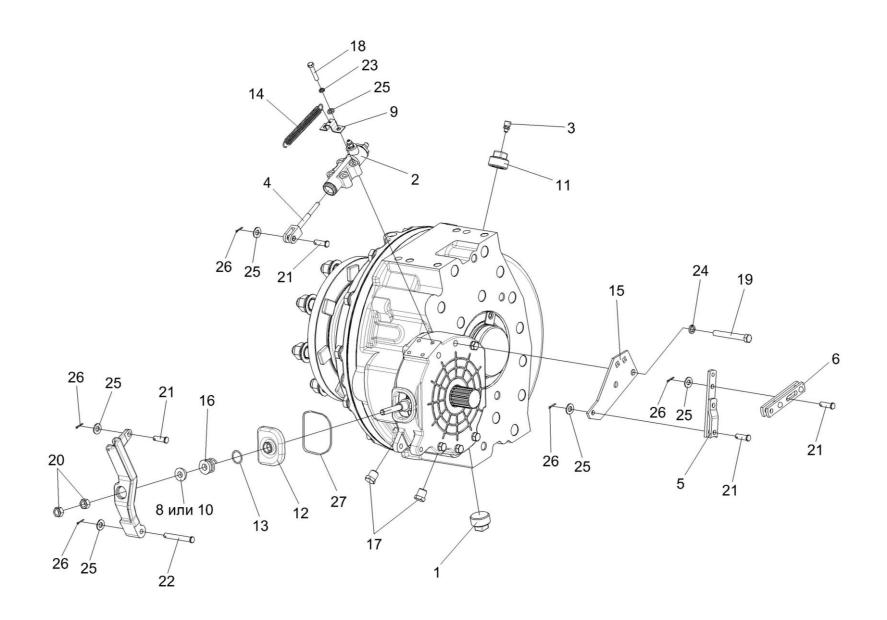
Редуктор бортовой левый УЭС 0107150-03
